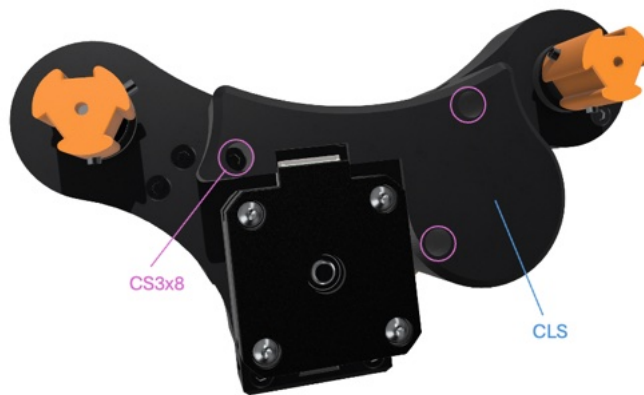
Rewinder-Chassis Montageschritt 28.
